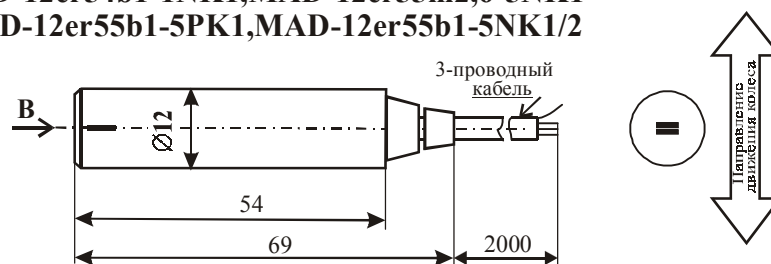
Внешний вид и габаритные размеры датчиков типа MAD-12er54b1-1NK1; MAD-12er55m2,6-5NK1, MAD-12er55b1-5PK1; MAD-12er55b1-5NK1/2
